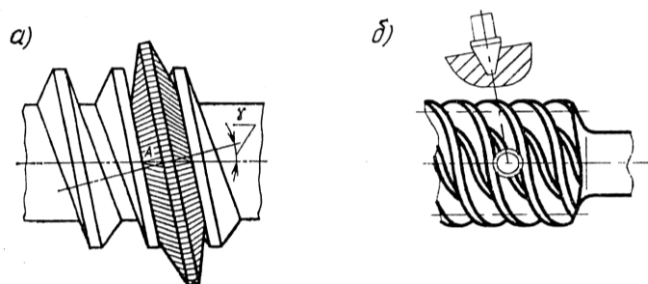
Схема установки дисковой фрезы с прямолинейным профилем при нарезании червяка ZK1 (а) и пальцевой фрезы при нарезании червяка ZK2 (б)
